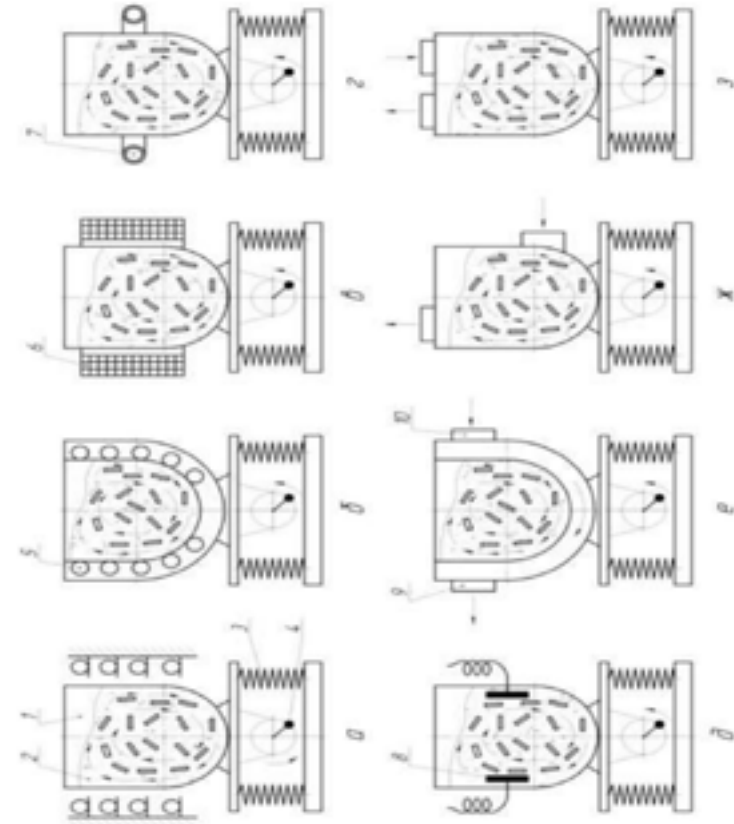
Схема виброустановки с различными резервуарами для механотермической обработки деталей
